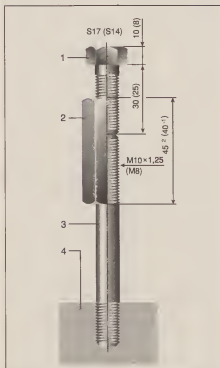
Приспособление для отворачивания шпилек: 1 – болт; 2 – гайка; 3 – шпилька; 4 – агрегат автомобиля.
